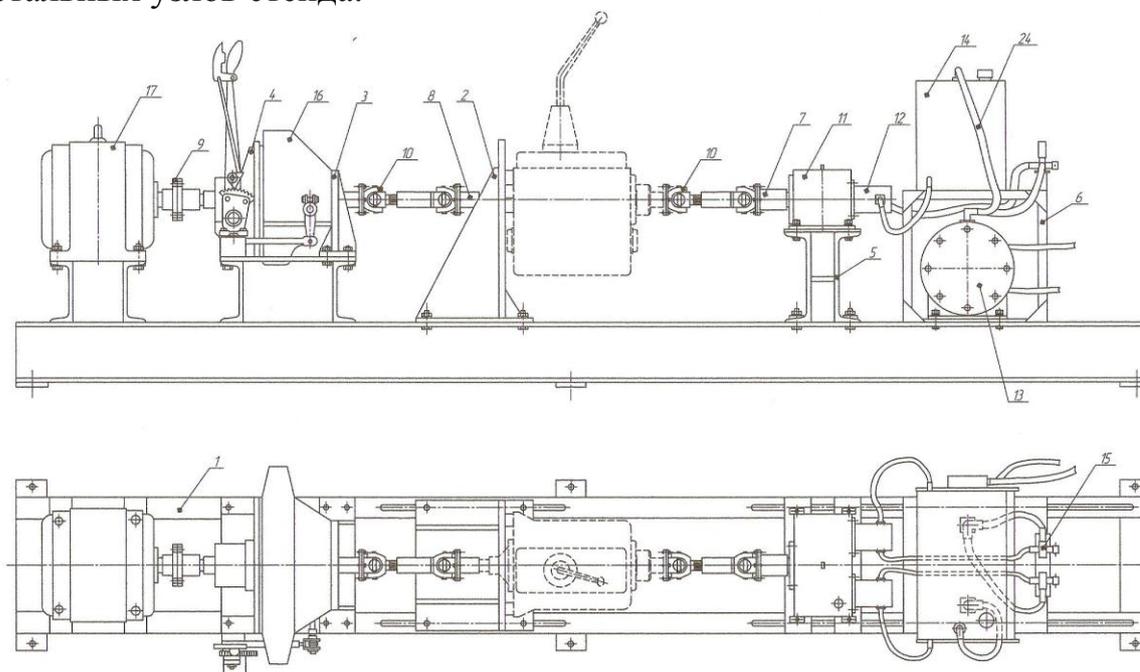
Стандарт обкатки КПП собственной конструкции
